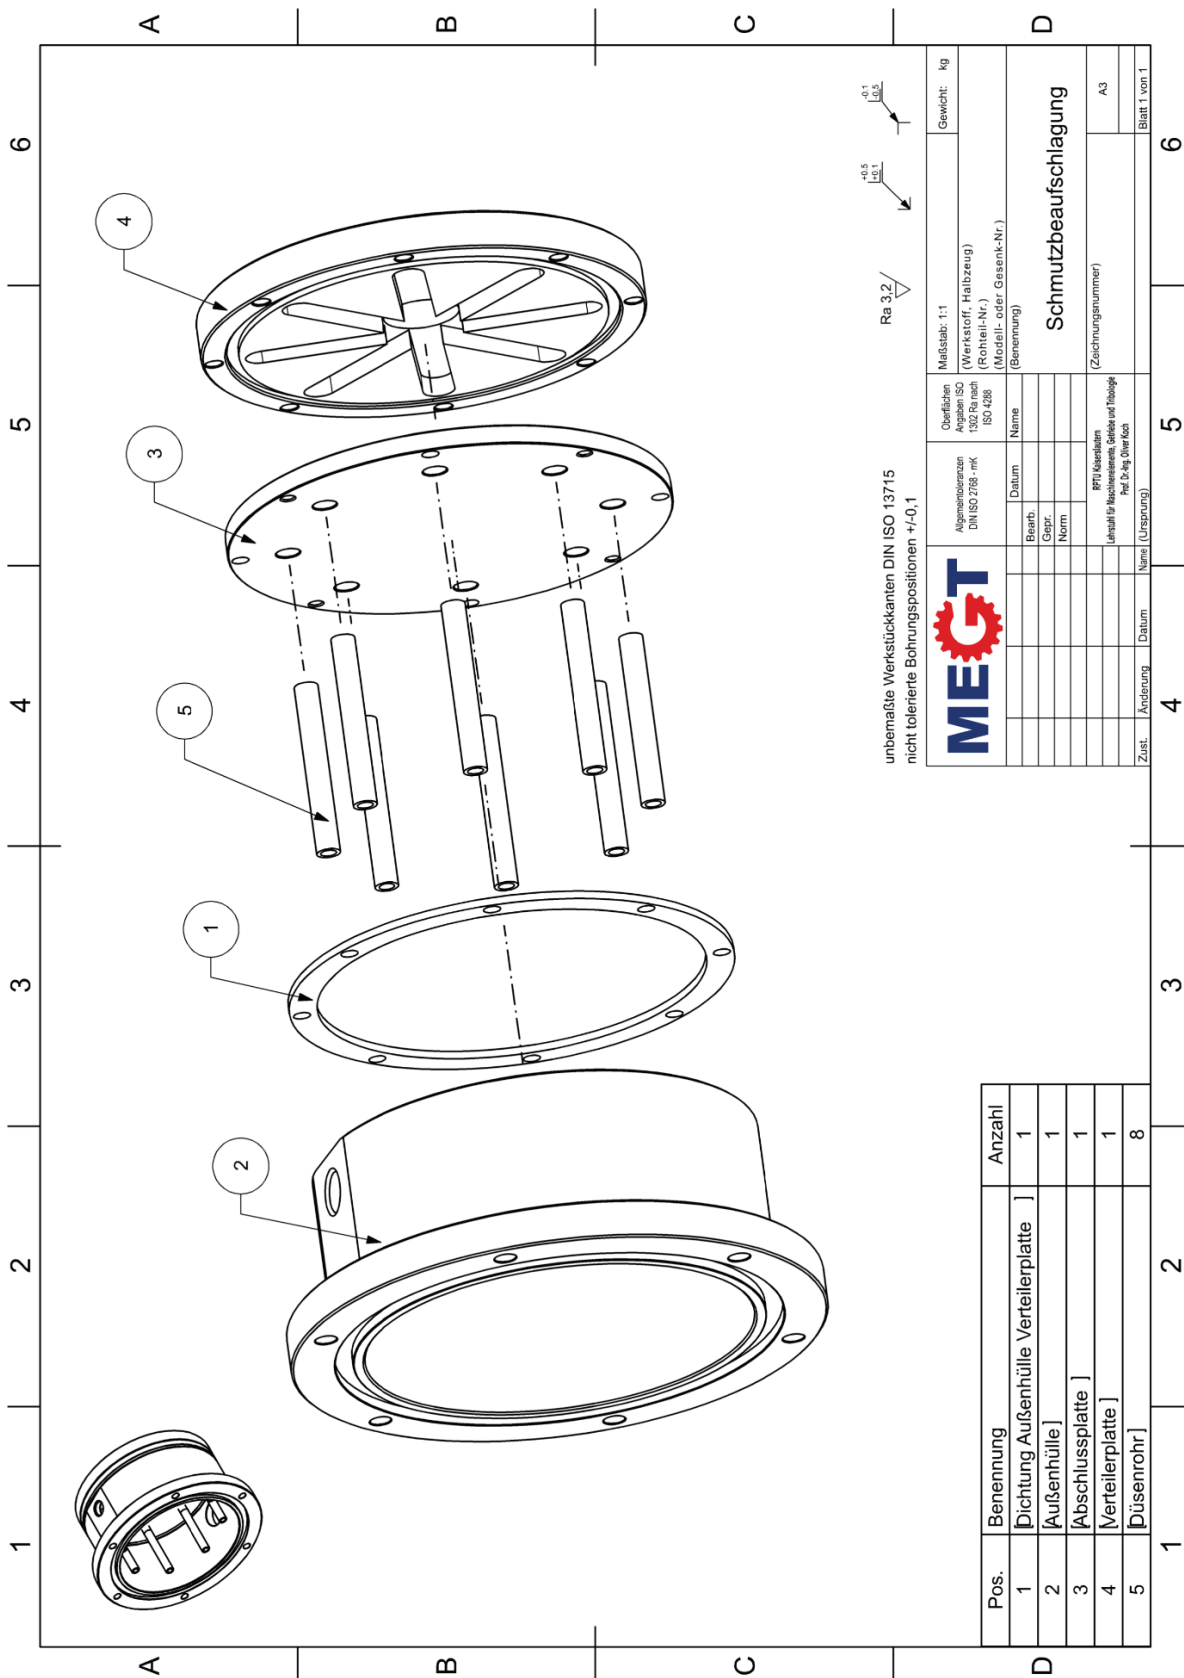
Explosionszeichnung Beaufschlagungseinheit
